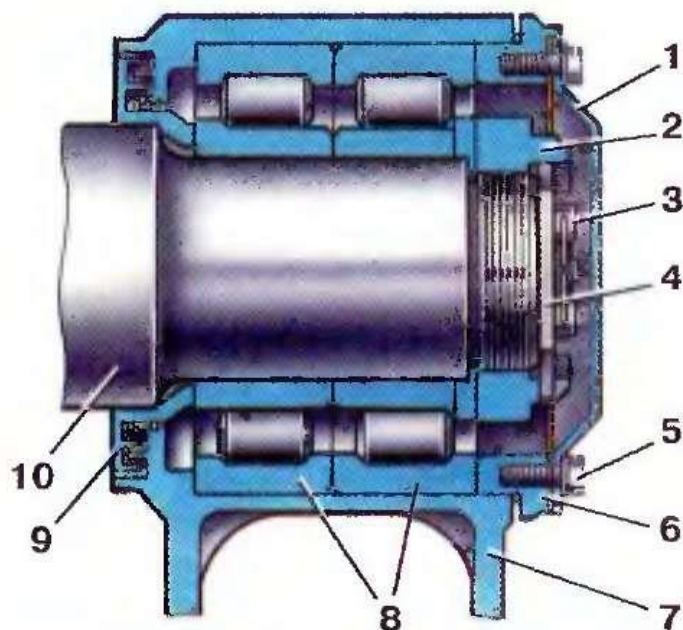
Буксовий вузол причіпного вагона: 1 – оглядова кришка; 2 – торцева гайка; 3 – болт; 4 – стопорна пластина; 5 – кришка; 6 – корпус букси; 7 – підшипник; 8 – лабіринтове кільце; 9 – лабіринтова кришка; 10 – вісь колісної пари
